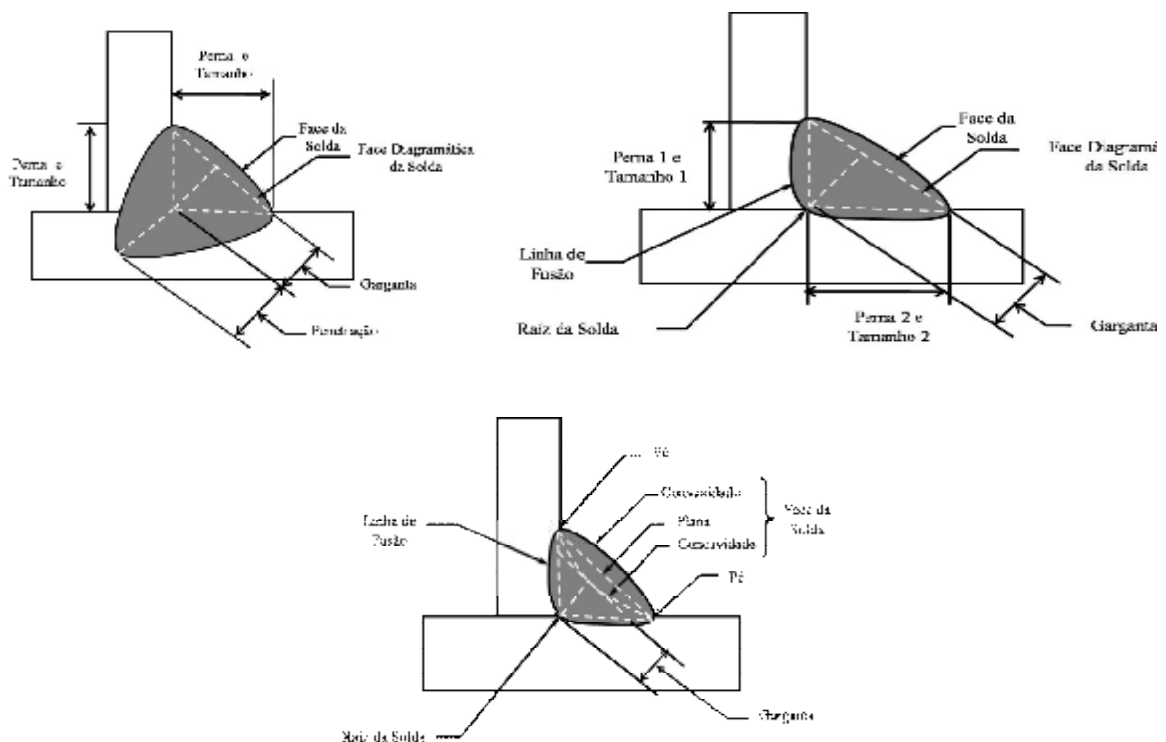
Forma e geometria do cordão de solda junta de filete “T”.
